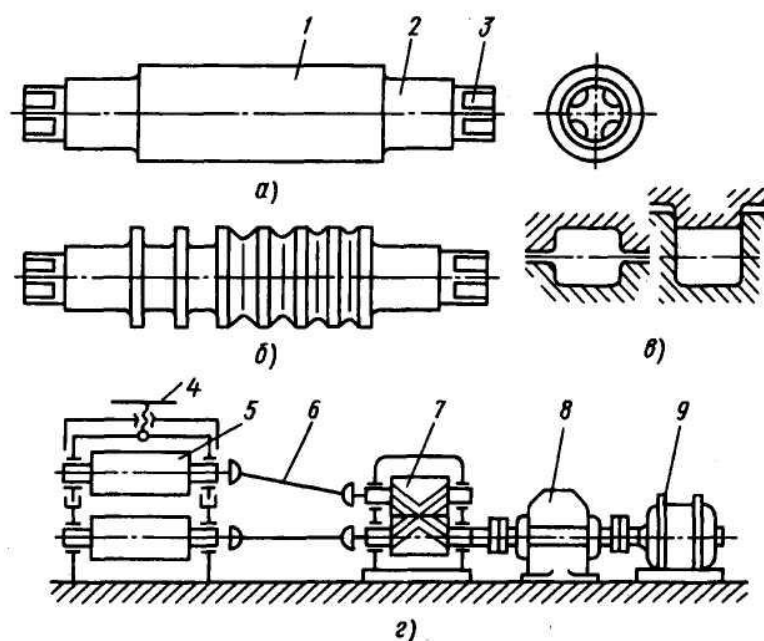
Валки и схема их привода в рабочей линии прокатного стана:
